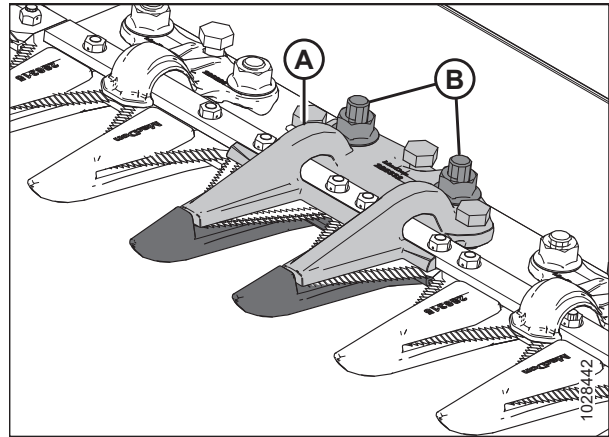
Загострений центральний протиріжучий палець ножа
